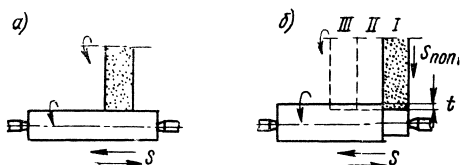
Схемы круглого наружного шлифования: а — с продольной подачей; б — комбинированным способом
